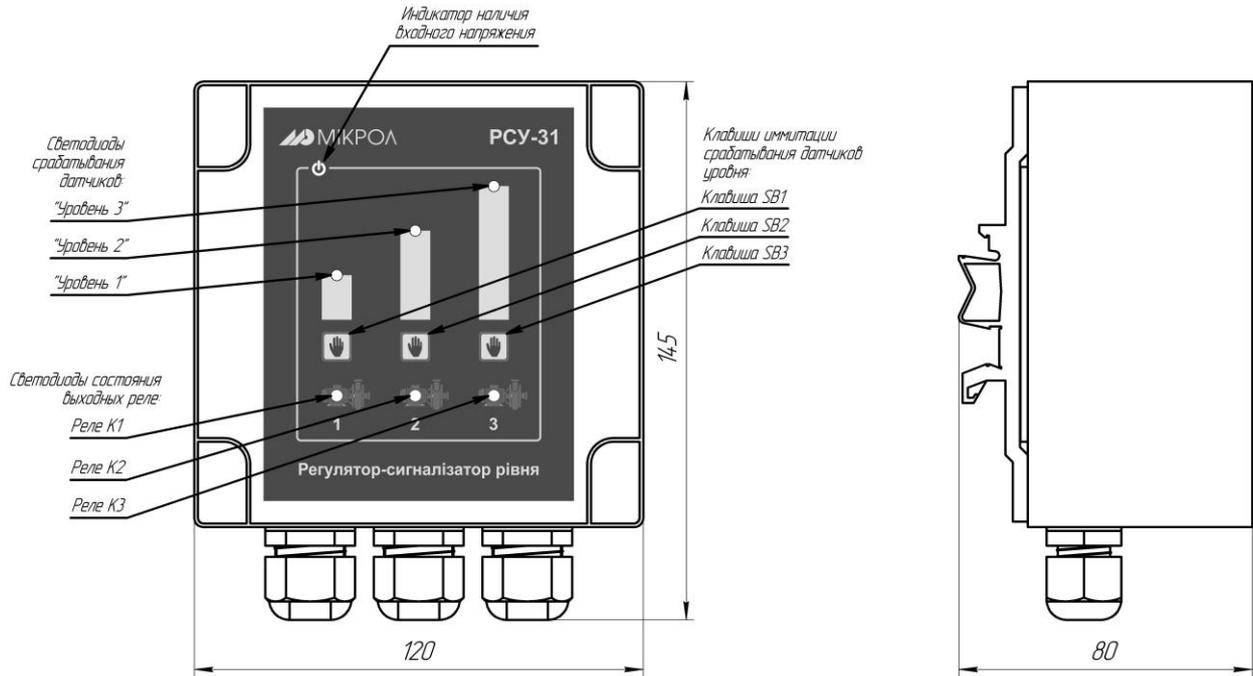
Внешний вид и габаритные размеры PCY-31
